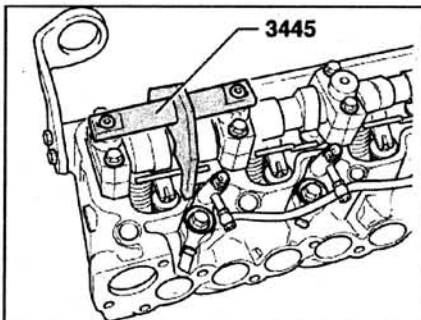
Заблокируйте распределительный вал, установив блокировочное устройство 3445 на кулачки 4-го цилиндра.
